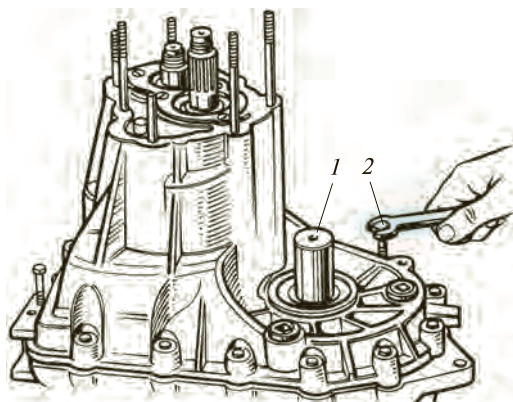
Завертывание упорных болтов в картер коробки и установка оправки в шестерню полуоси:
